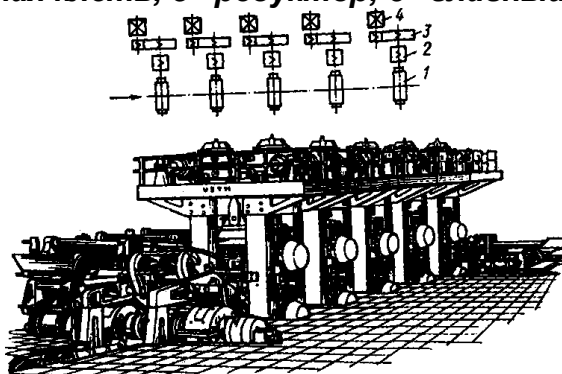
Непрерывный многоклетьевой стан: а - схема расположения рабочих клеток и их приводов; б - общий вид стана; 1 - рабочие клетки; 2 - шестеренные клетки; 3 - редукторы; 4 - главные электродвигатели
